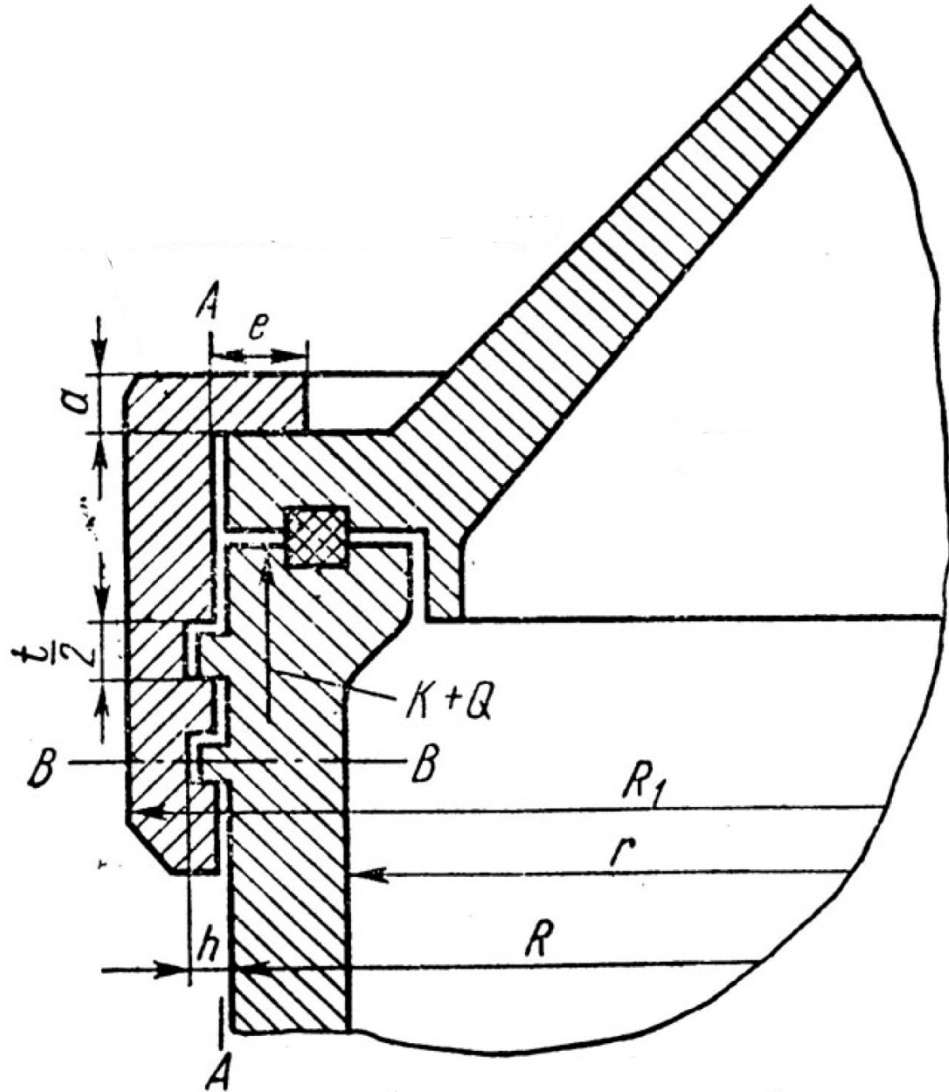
Розрахункова схема з'єднувального кільця сепаратора.
